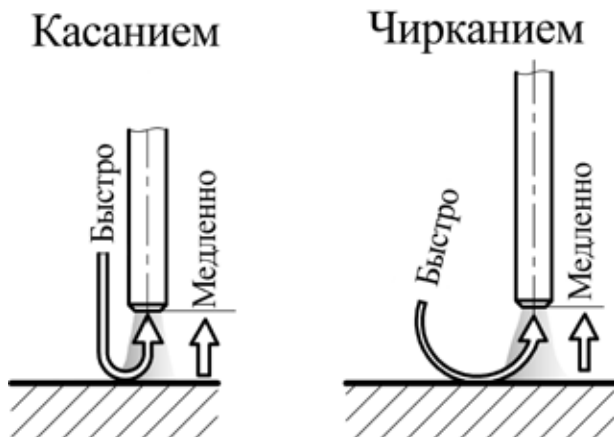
Способы зажигания сварочной дуги.
